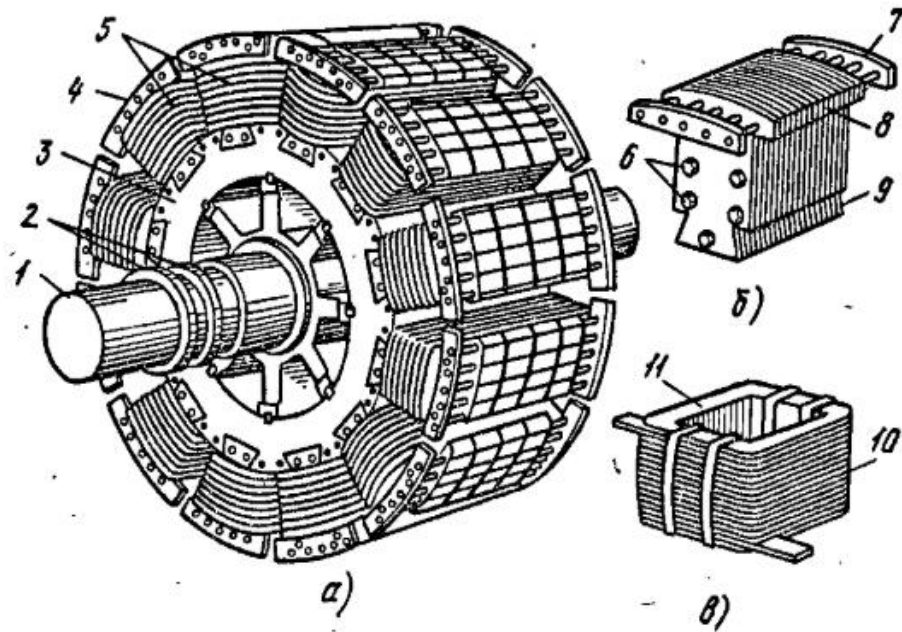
Конструкція явнополюсного ротора і його деталей:
